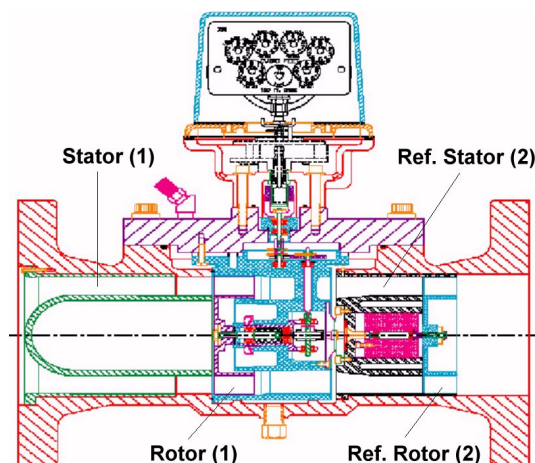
Querschnitt des AccuTestTM Turbinenradgaszählers
